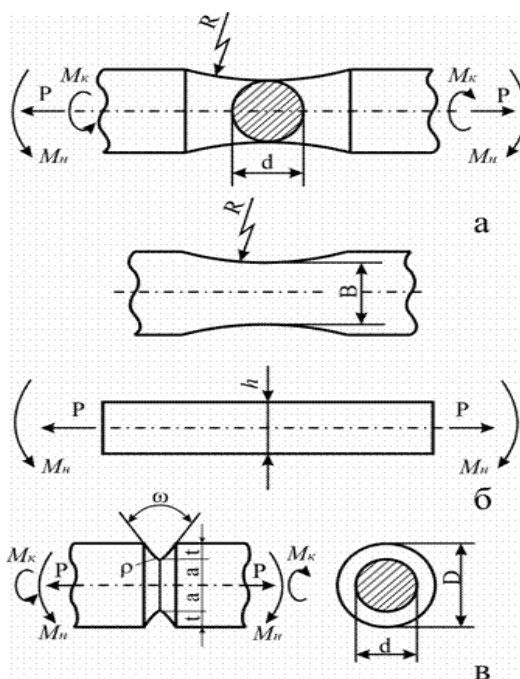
Форма и основные размеры рабочей части стандартных образцов для испытаний на усталость
